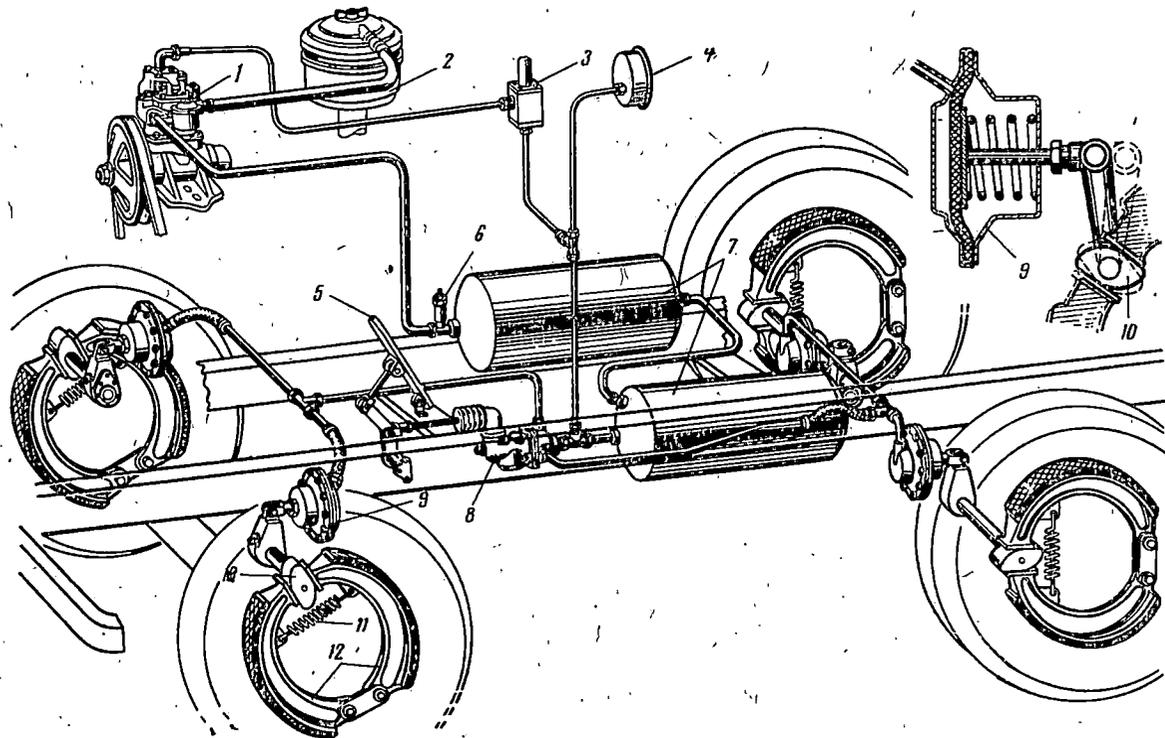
Схема ножного тормоза с пневматическим приводом:
